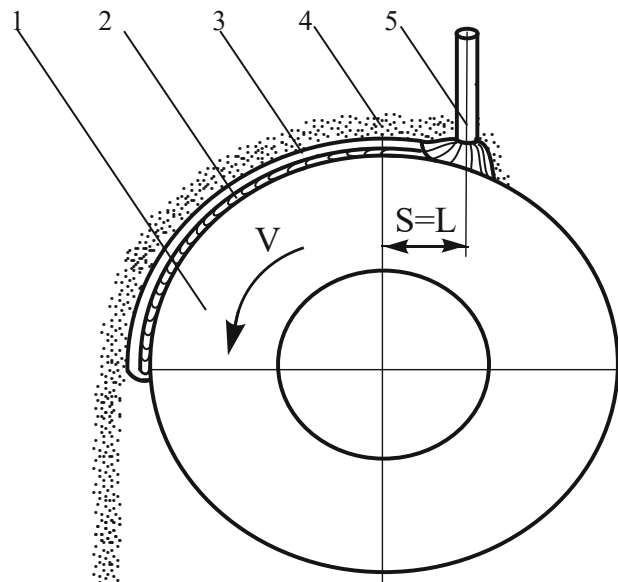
Зміщення електроду з zenіту у напрямку, протилежному до обертання деталі, на величину зварювальної ванни: 1 – циліндрична деталь; 2 – наплавлений метал; 3 – шлак; 4 – флюс; 5 – електрод
